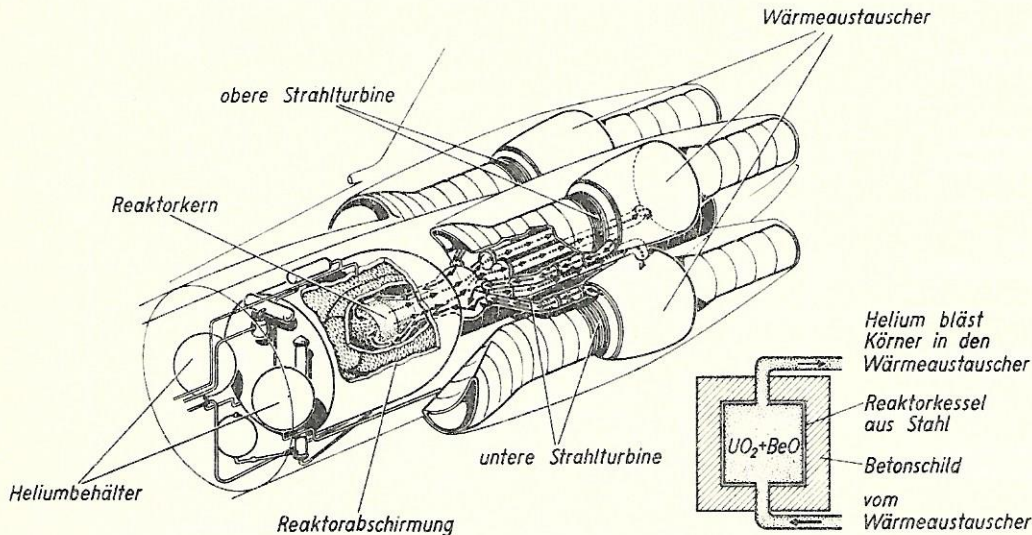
Reaktortriebwerk für Flugzeuge (De Havilland)
